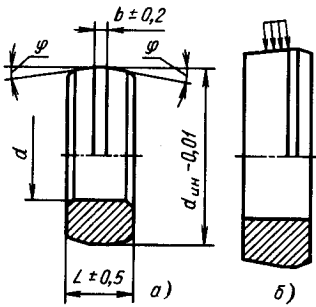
Деформирующий элемент сборной оправки: а — симметричный; б — симметрично-нагруженный
